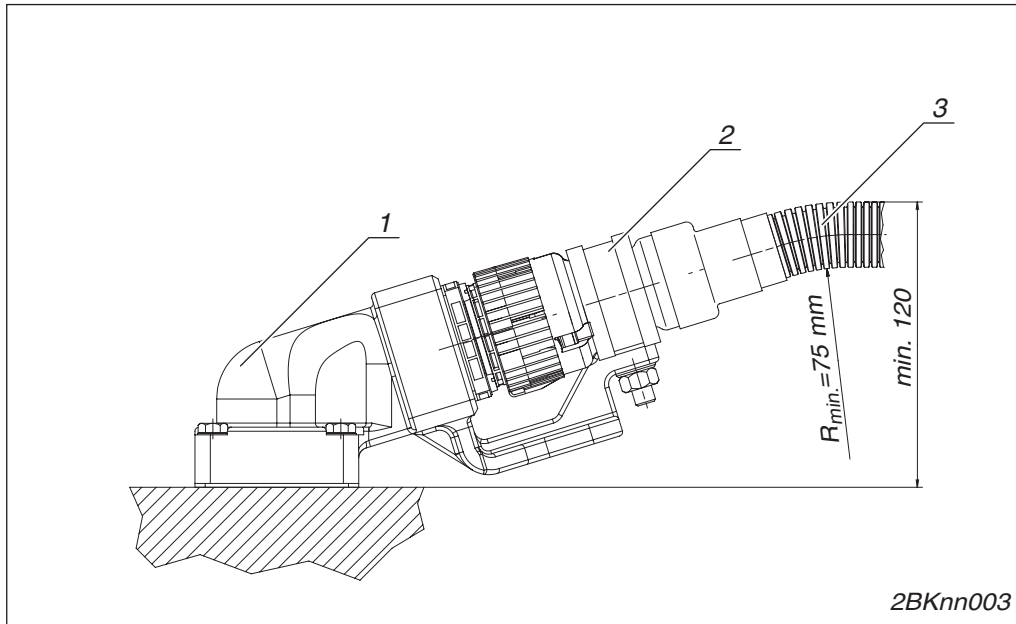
Steckverbindung Getriebe 17° - Getriebekabel (Kabel1)
